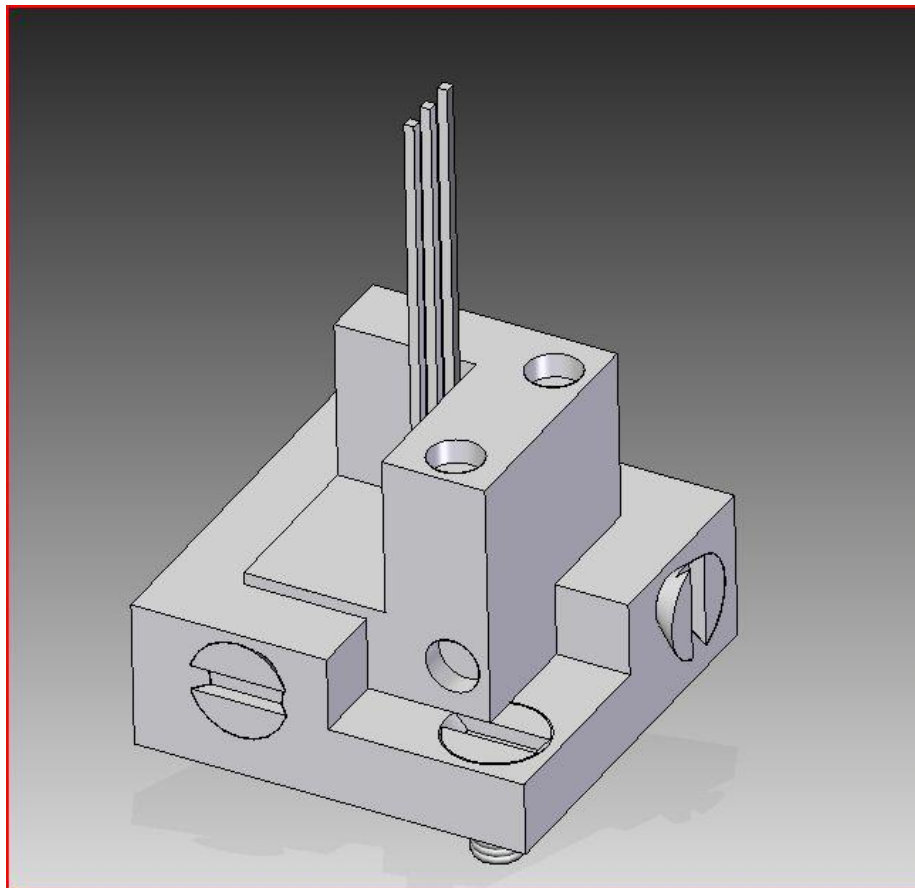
Diseño final en Solid Edge de cubo seccionado, posición 3
